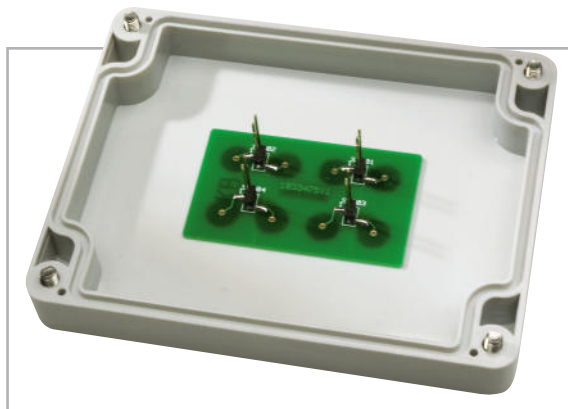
Tastenplatine, in IP-65-Gehäuse geklebt
